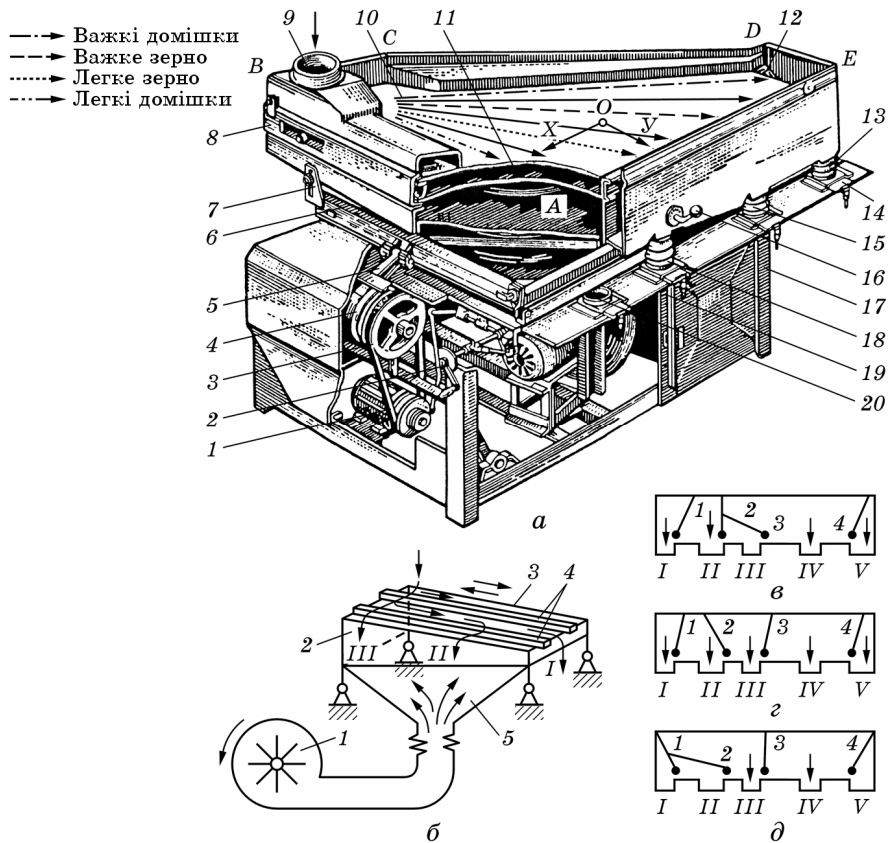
Пневматичний сортувальний стіл ПСС-2,5В:
